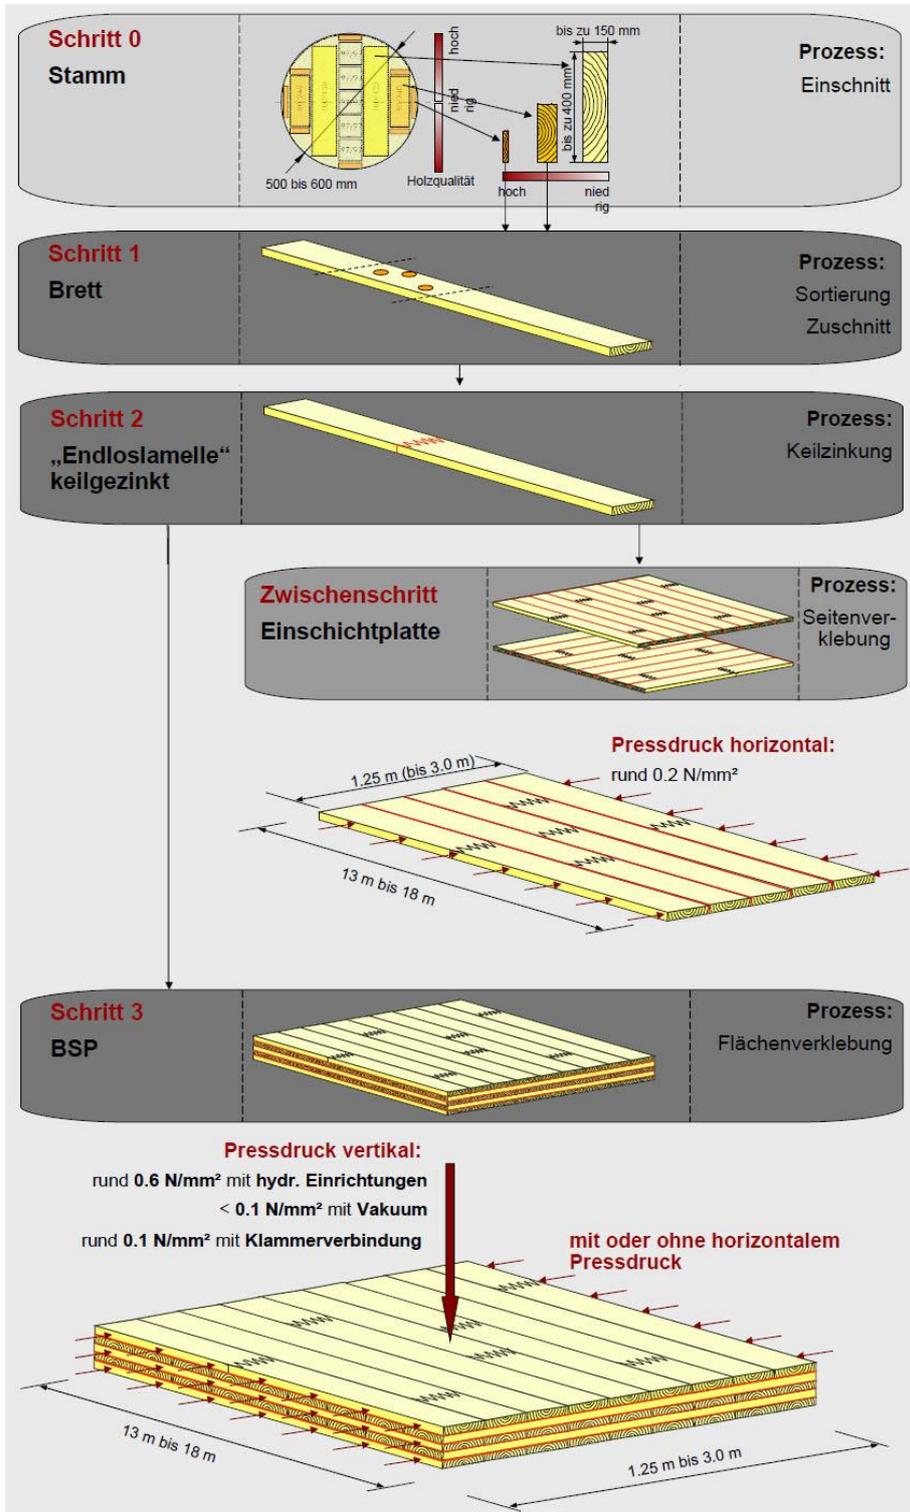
Produktionsprozess Brettsperrholz – Deckenelement³⁶
